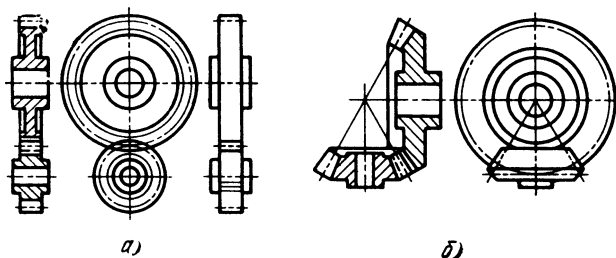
Условное изображение зацеплений цилиндрическими (а) и коническими (б) зубчатыми колесами
